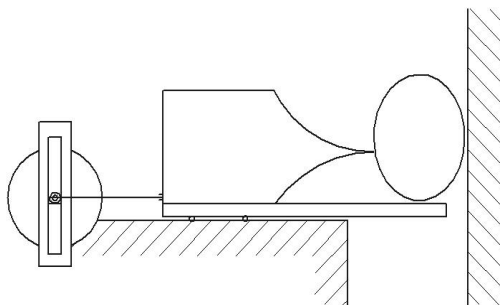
Блок ножей, выполненный в виде пластины с опорными полочками
